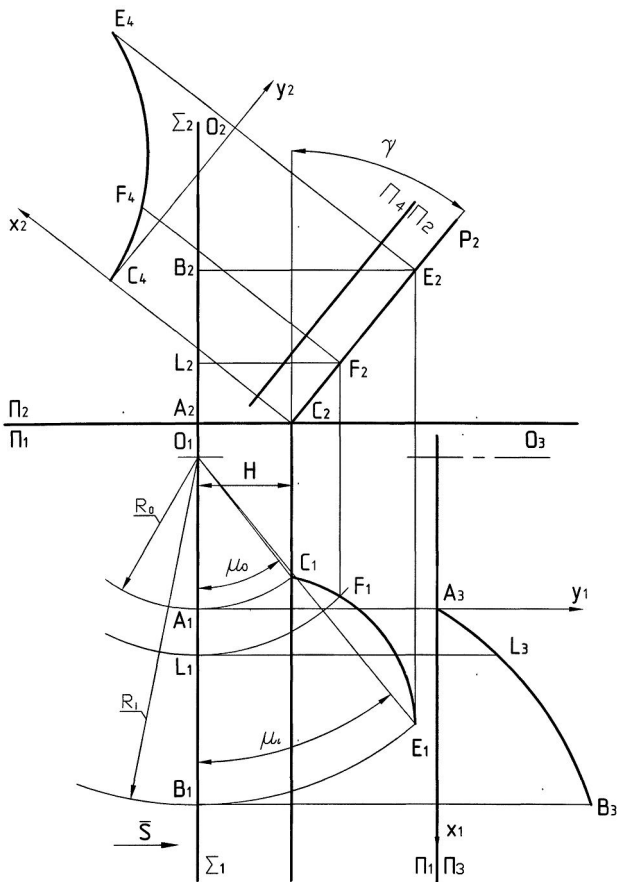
Графічне визначення профілю циліндричної поверхні деталі, обробленої торцевою фрезою
